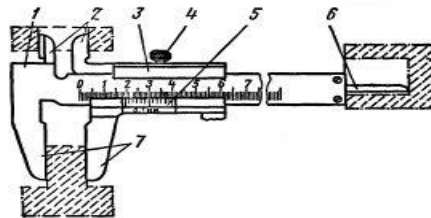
Штангенциркуль та схема його використання при вимірюванні зовнішніх і внутрішніх розмірів деталей (заштриховані): 1 – штанга; 2,7 – губки; 3 – рухома рамка; 4 – затискач; 5 – шкала ноніуса; 6 – лінійка глибиноміра [3]
